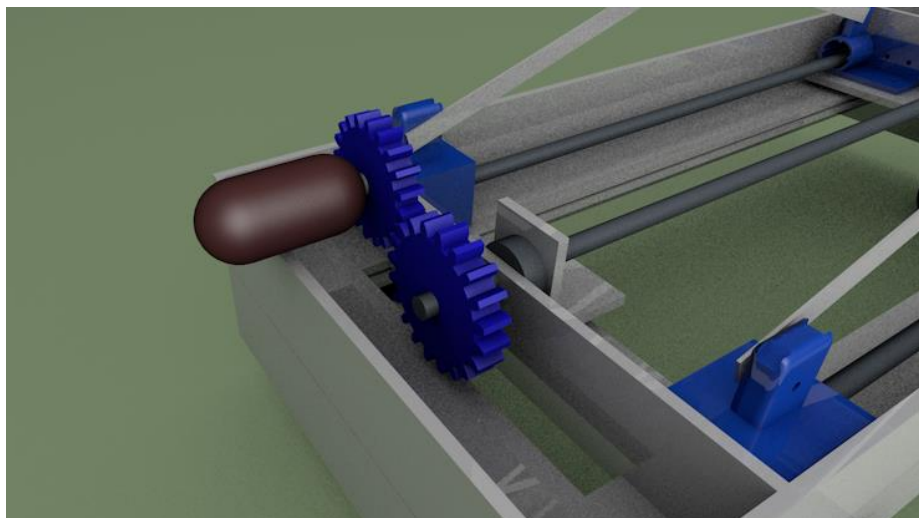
Engranajes para transmitir el movimiento del motor al tornillo.
